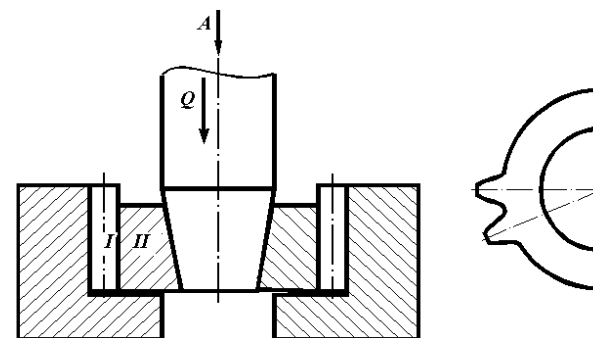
Схема калибровки зубьев шестерни с радиальным течением металла
